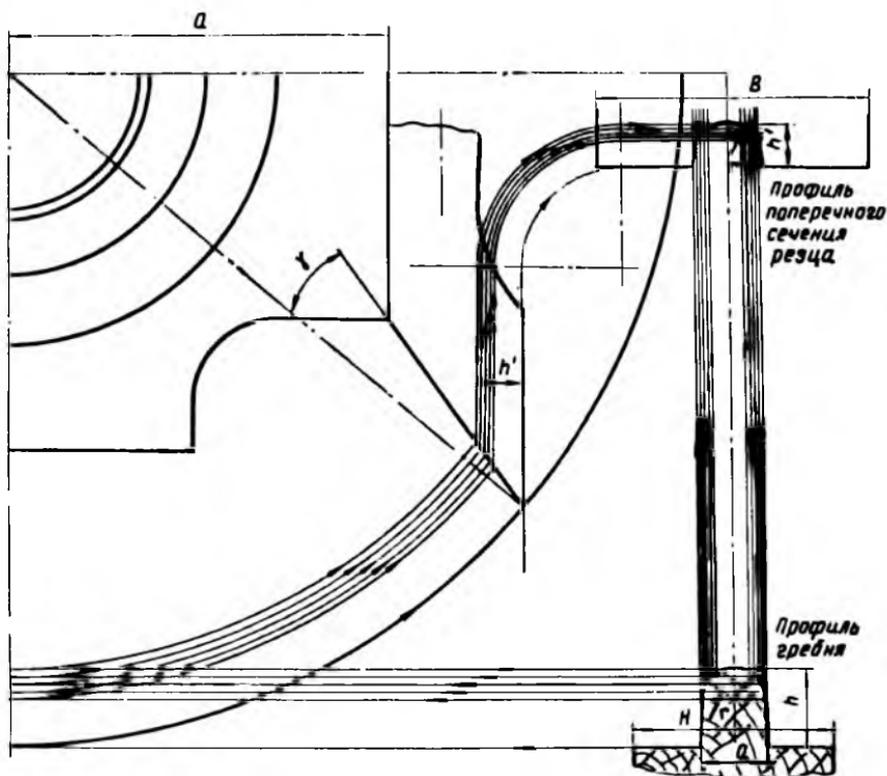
Графическое построение профиля поперечного сечения резца по профилю изделия
